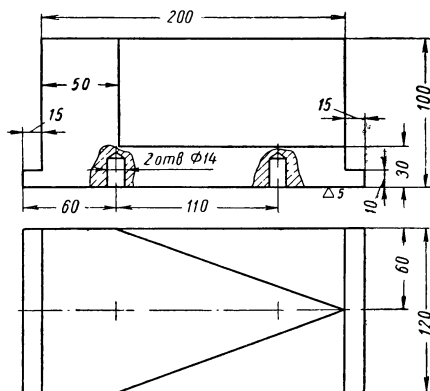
Чертеж обрабатываемой детали переменной ширины
